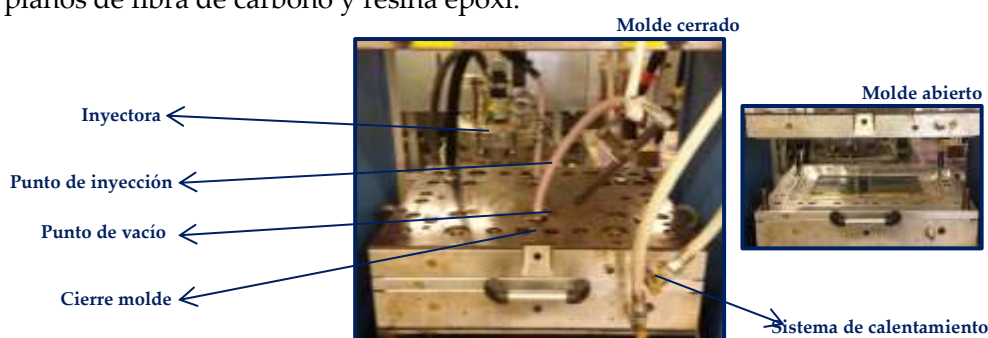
Molde para la obtención de paneles planos por moldeo por transferencia de resina o RTM. Propiedad de Eureka.
